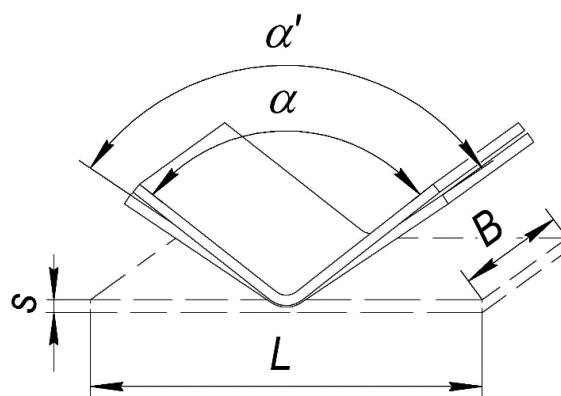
Схема формування заготовок: L – довжина заготовки, S – товщина заготовки, B – ширина полиці, α – кут підгину штампа, α' – кут після зняття навантаження
